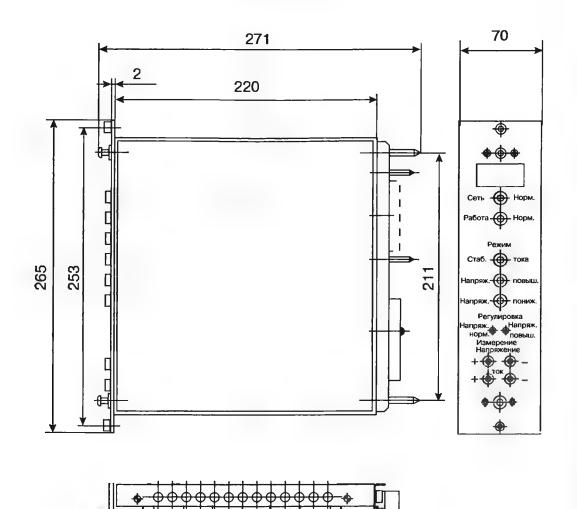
Общий вид блоков БПС-30В/10А-12(14) и их габаритные размеры
